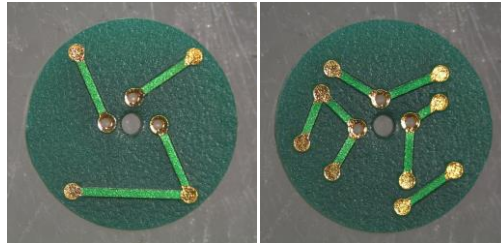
Photos du PCB porte-puces : (à gauche) face avant ou côté PyroMEMS ; (à droite) face arrière.
